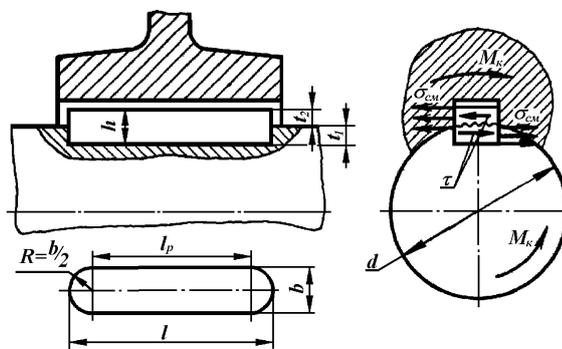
Неподвижное соединение призматической шпонкой.
